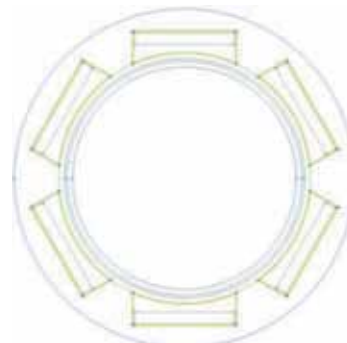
Конструкция предлагаемой установки индукционного нагрева
